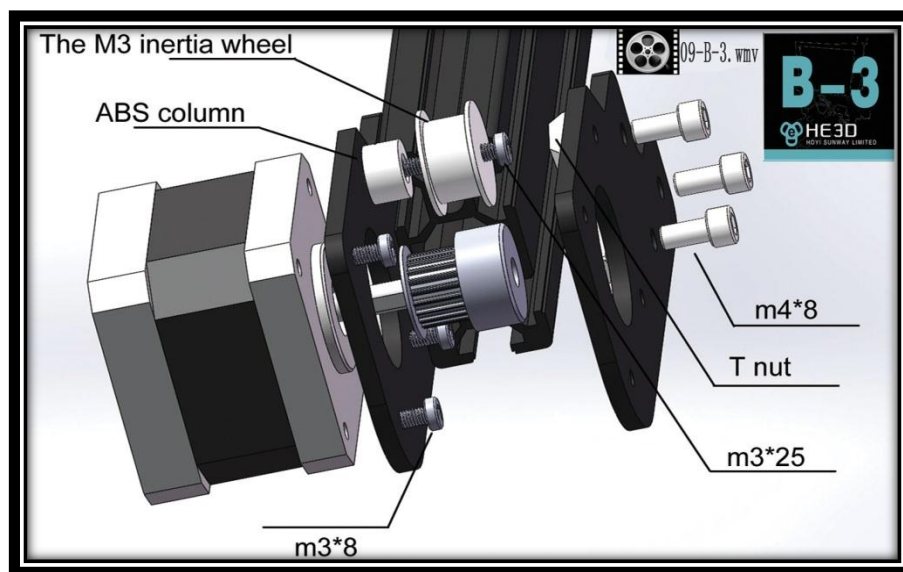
Motor paso a paso que moviliza el carrito del hotend, extremo izquierdo del eje Y.
